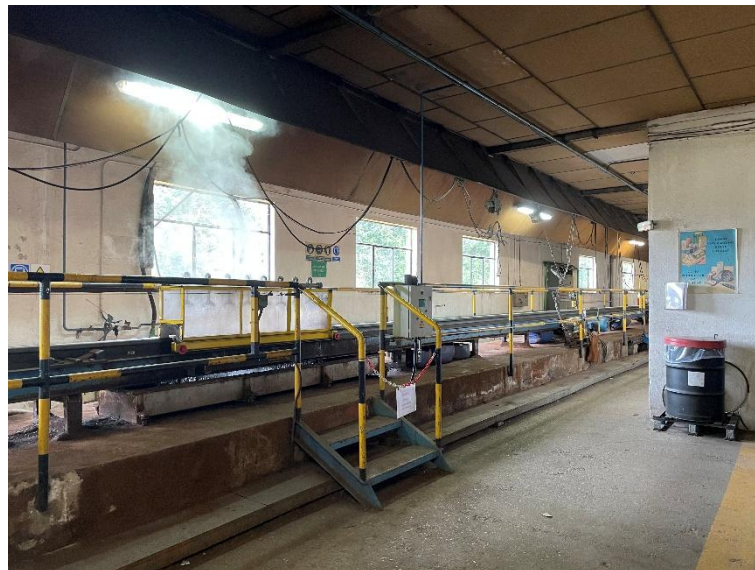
Grifos de refrigeración de soldadura. Fuente: Propia
